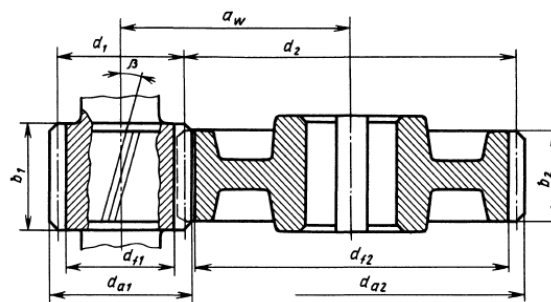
Геометрические параметры цилиндрической зубчатой передачи
